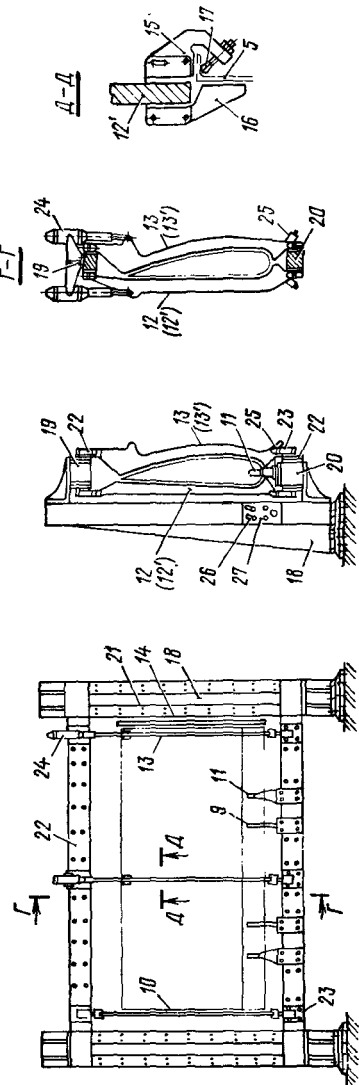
Схема базирования, схема сборки и сборное приспособление для сборки тормозного щитка
